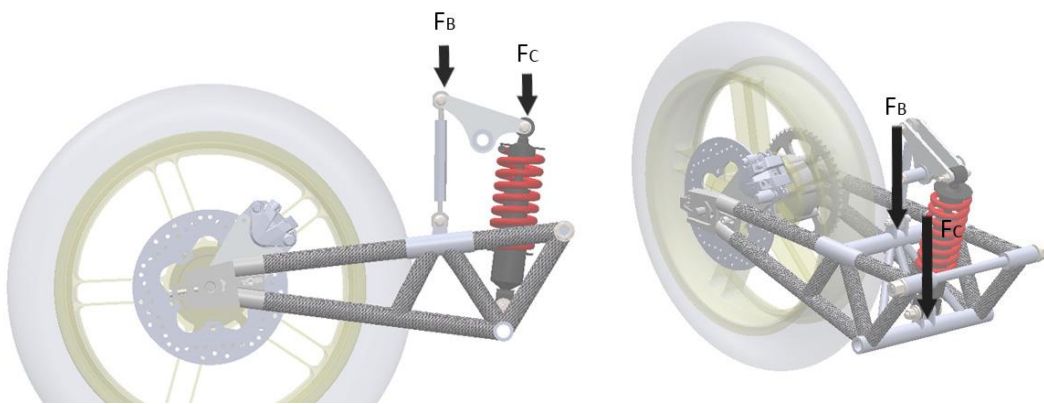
Esquema de las fuerzas del balancín que recaen en el basculante
